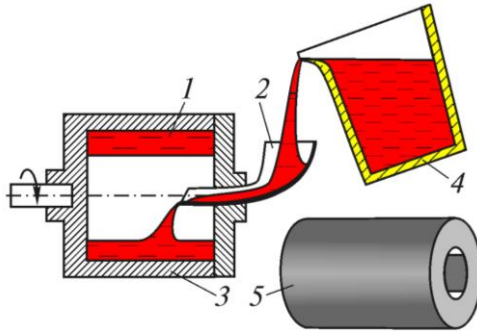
Схема відцентрового лиття порожнистих циліндрових заготовок у машині з горизонтальною віссю обертання: 1 – розплав; 2 – жолоб; 3 – виливниця, що обертається; 4 – ківш із металом; 5 – виливок [24]
